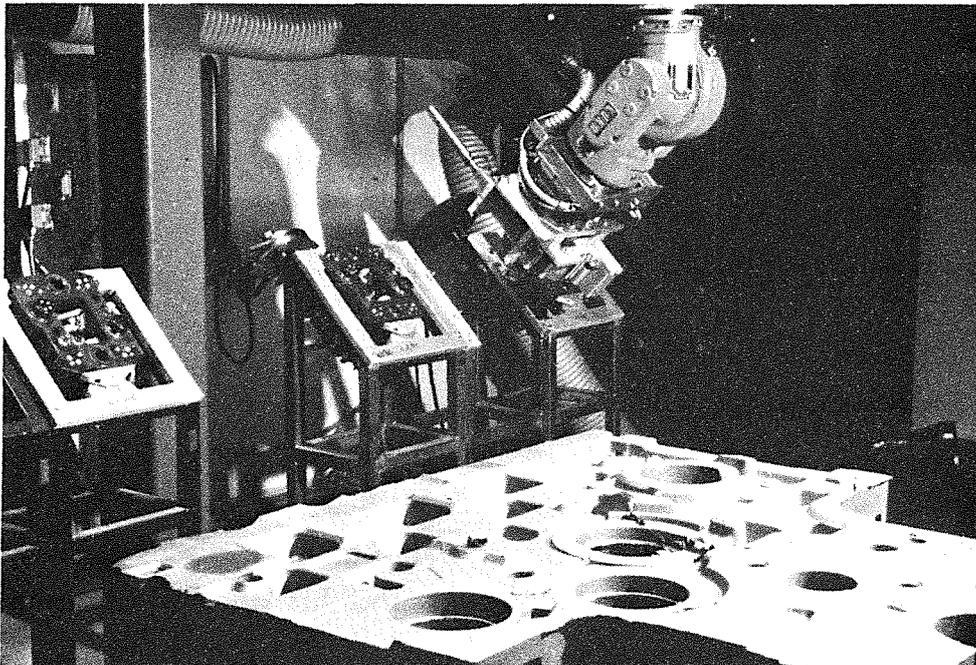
COMETOS mit einer Druckmaschinenseitenwand
